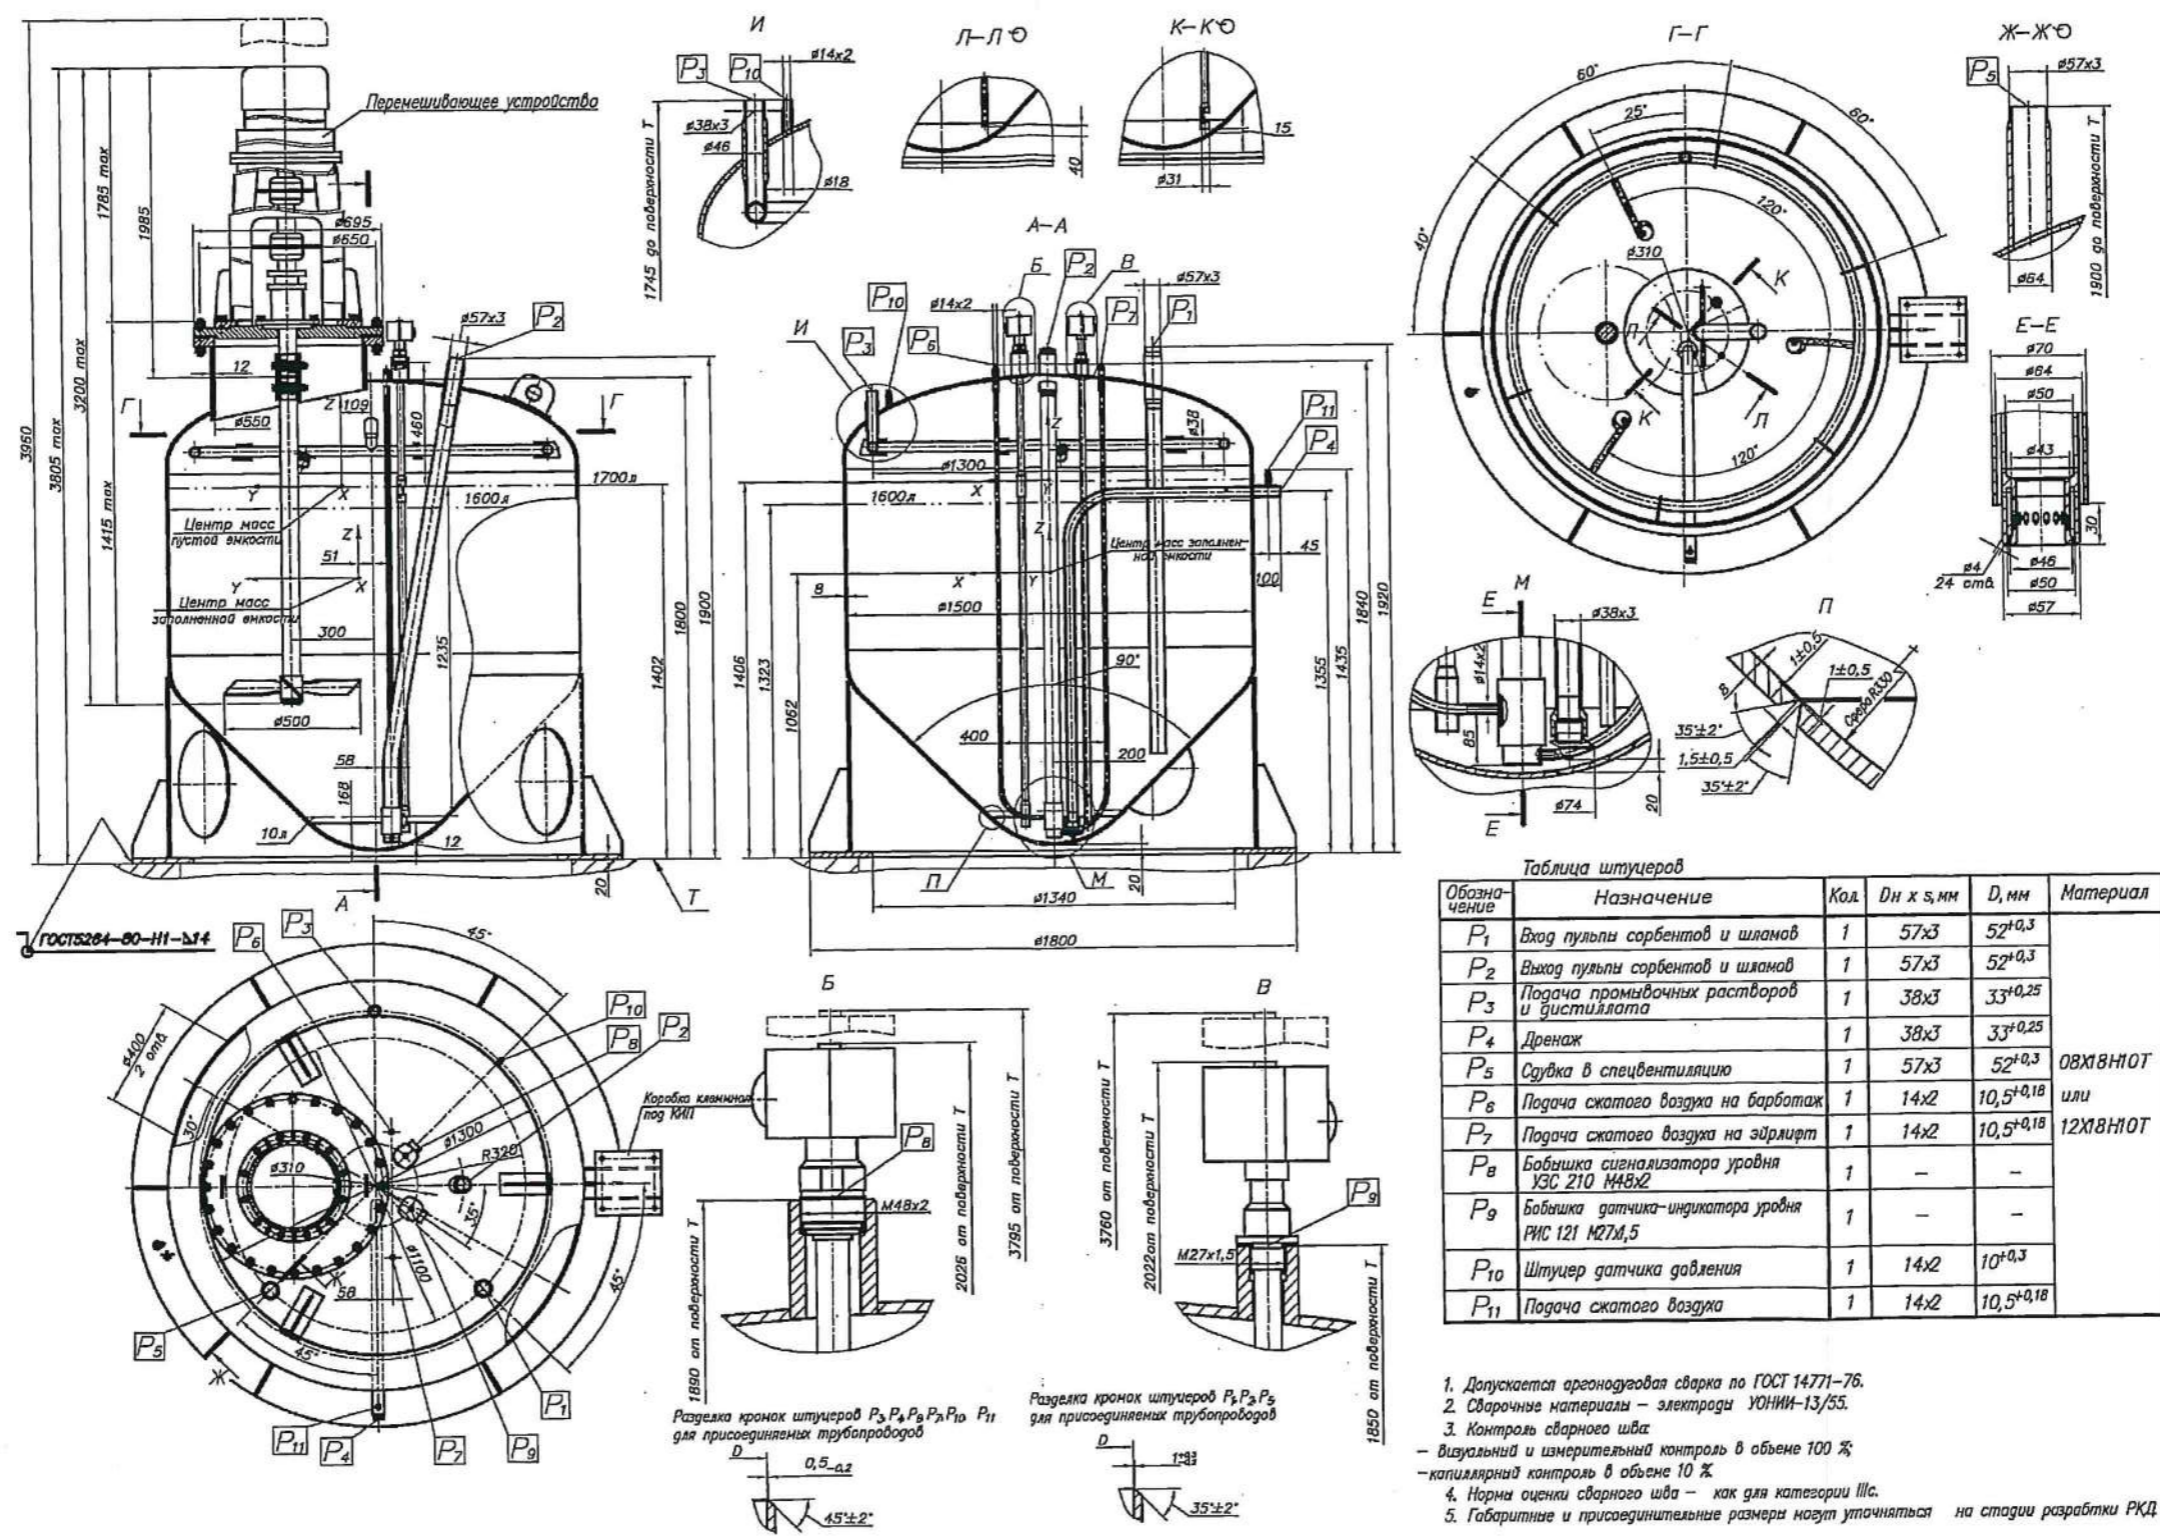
Габаритные, присоединительные размеры и конструктивное устройство емкости
